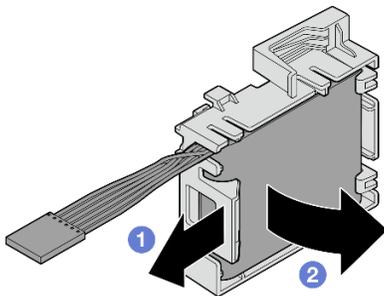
Rimozione del modulo di alimentazione flash RAID dalla staffa
